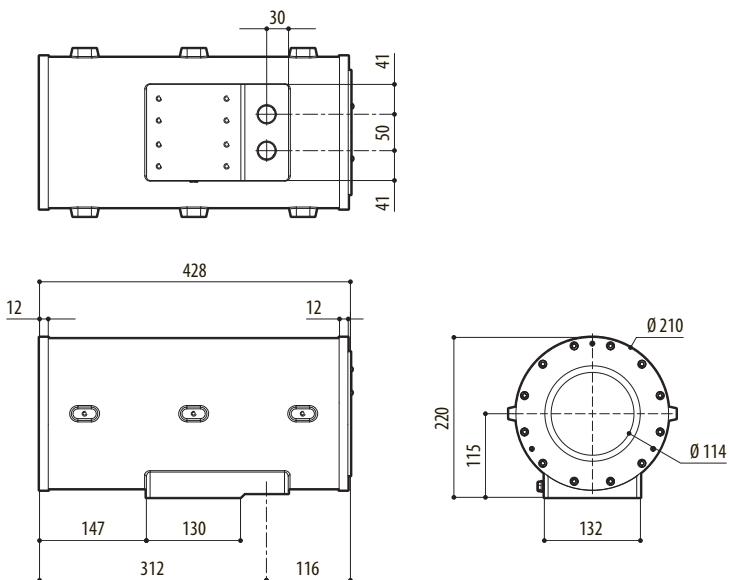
EXH (Fenster mit gehärtetem, extra-klarem Glas).
